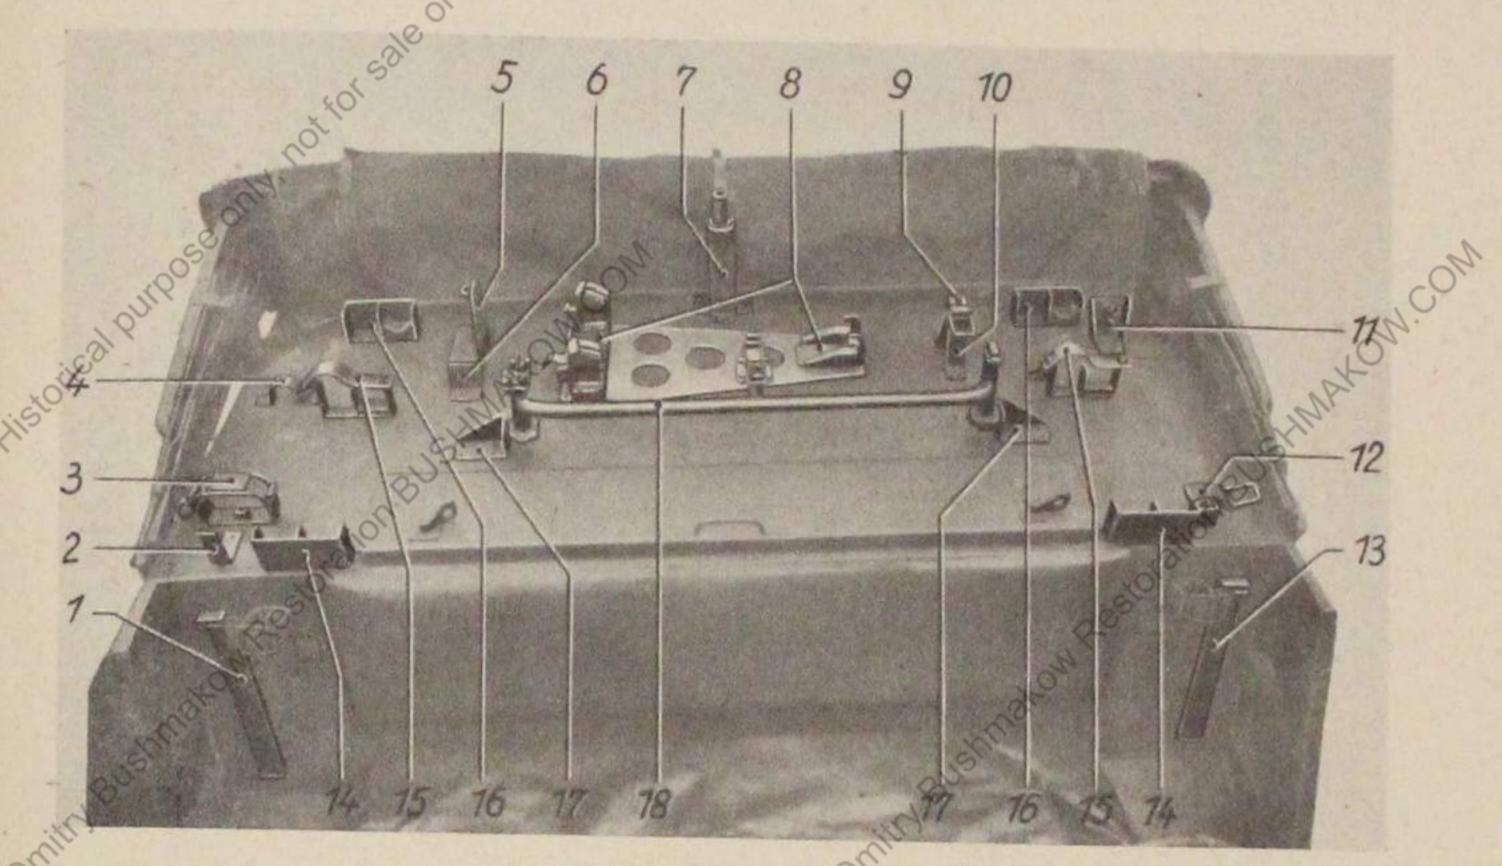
Befestigungsvorrichtungen auf dem hinteren Gerätraum, angebaut
